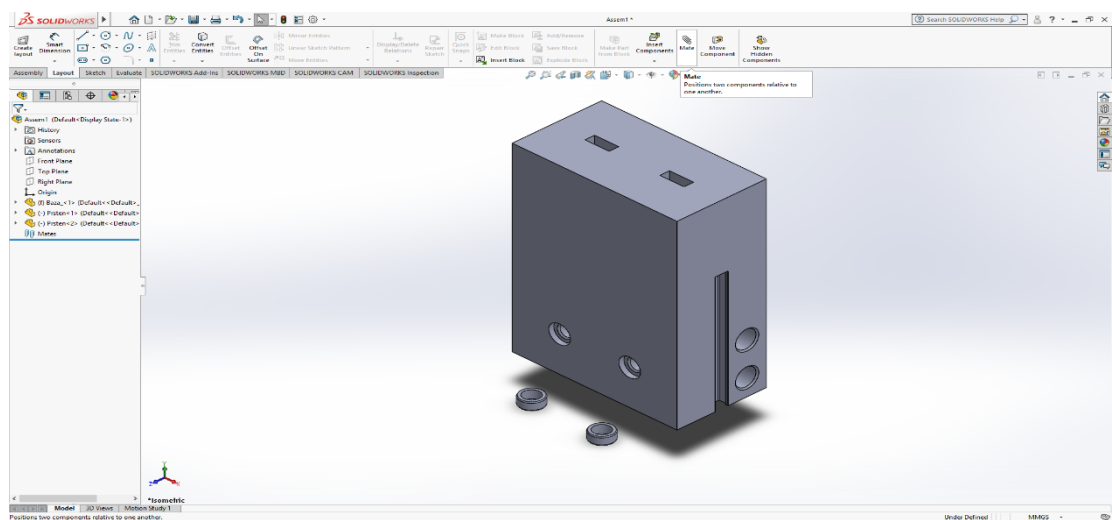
Stvaranje sklopa (eng. *Assembly-a*)
